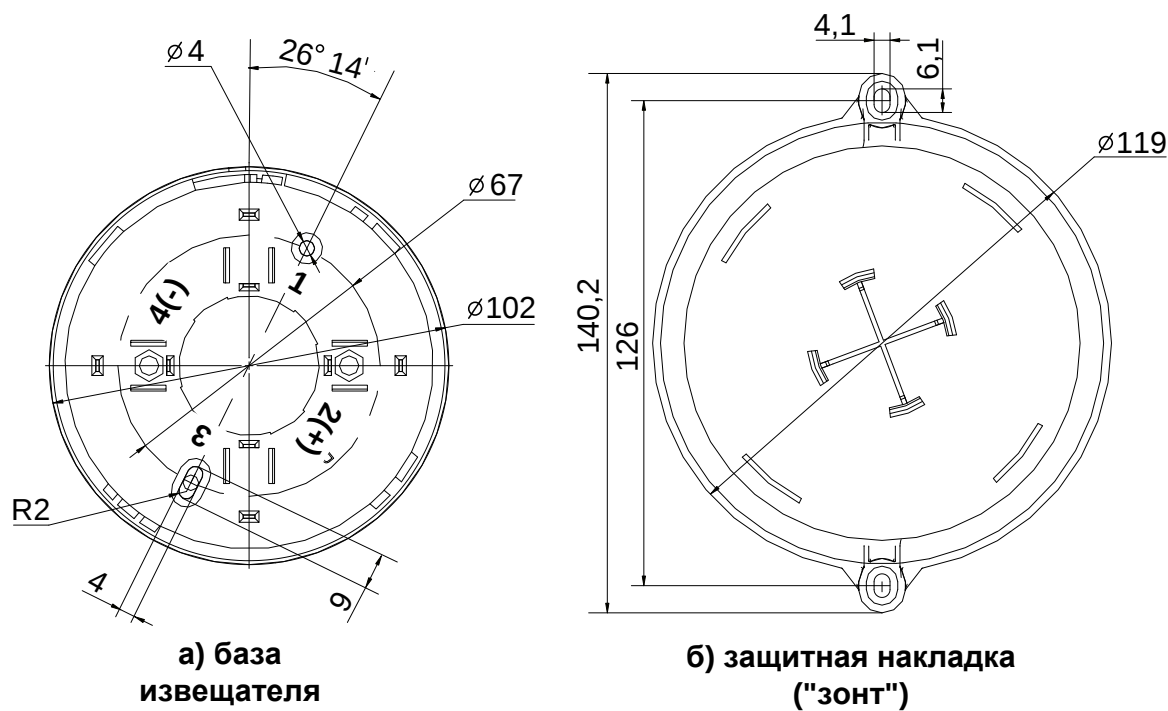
Габаритные и присоединительные размеры базы и защитной накладки «зонт»
